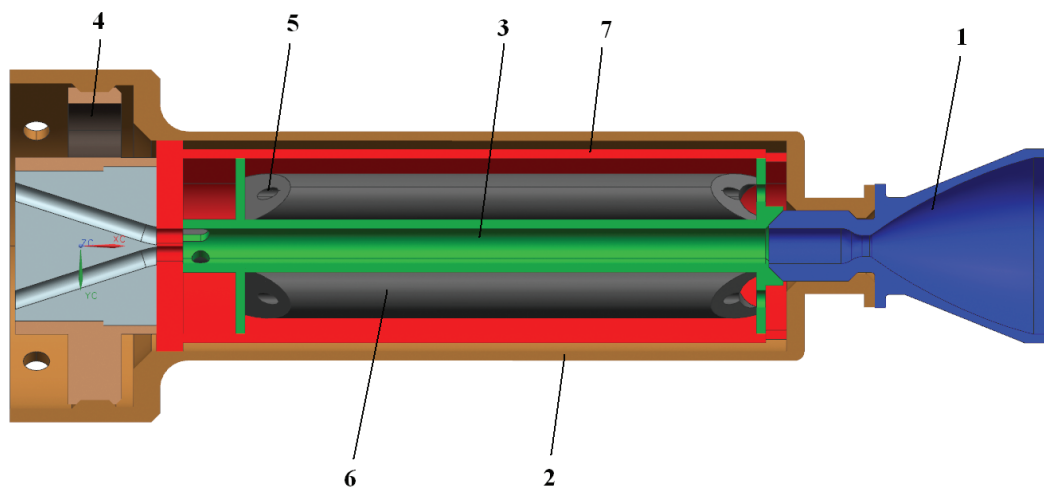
Схема ЭТМД: 1 — сопло Лавала; 2 — стакан камеры; 3 — полость газовада; 4 — пустотелая гайка; 5 — полость размещения нагревательного элемента; 6 — двухканальная керамическая трубка; 7 — цилиндрический стакан
